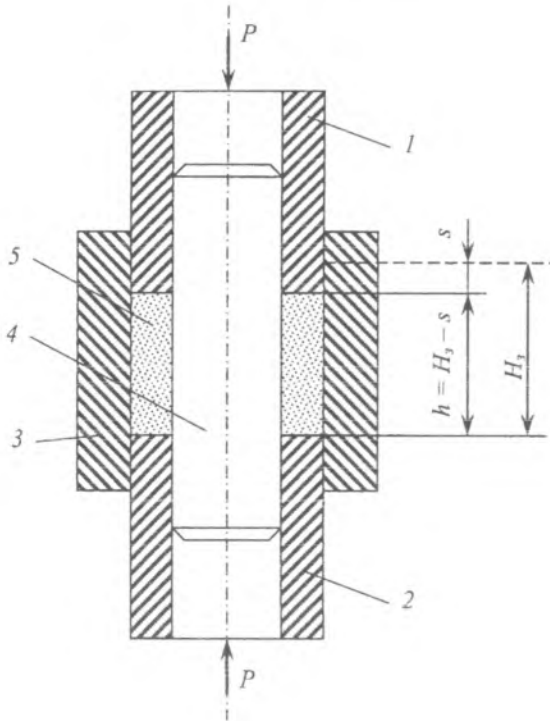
Схема двухстороннего прессования металлопорошка. 1 и 2 – трубчатые пуансоны, 3 – матрица, 4 – оправка, 5 – металлический порошок
